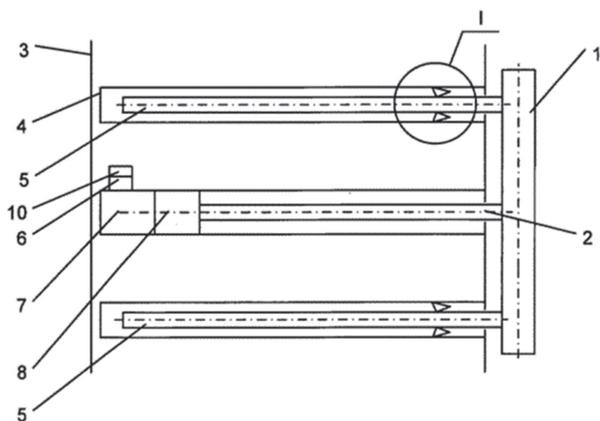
Вид устройства для предотвращения опрокидывания транспортного средства сверху: 1 – упор; 2 – толкатель; 3 – стенка транспортного средства; 4 – труба; 5 – стержень; 6 – пиропатрон газогенератора; 7 – цилиндр; 8 – поршень; 10 – датчик углового положения транспортного средства
